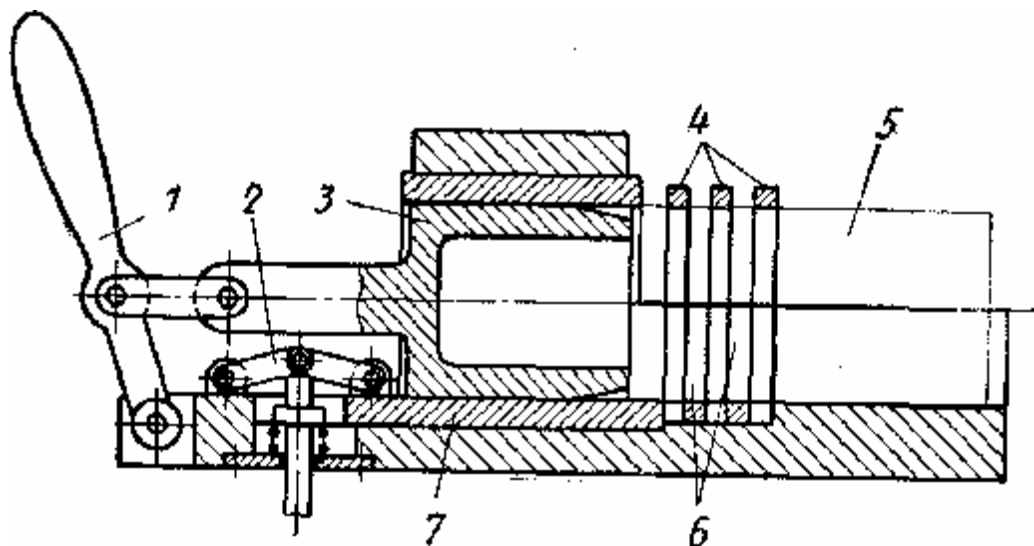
Пристосування для установки поршневих кілець на поршень
